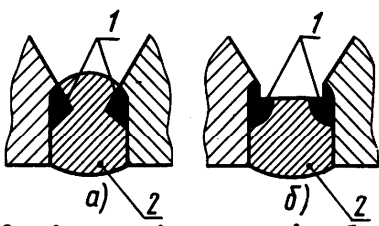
Шлифовка корня шва абразивным кругом: а - до шлифовки; б - после шлифовки; 1 - шлак; 2 - наплавленный металл
